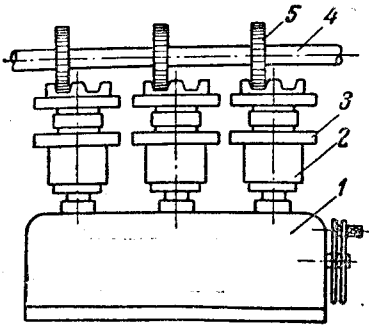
Резьбовая оправка для крещения регулировочной гайки при фрезеровании
